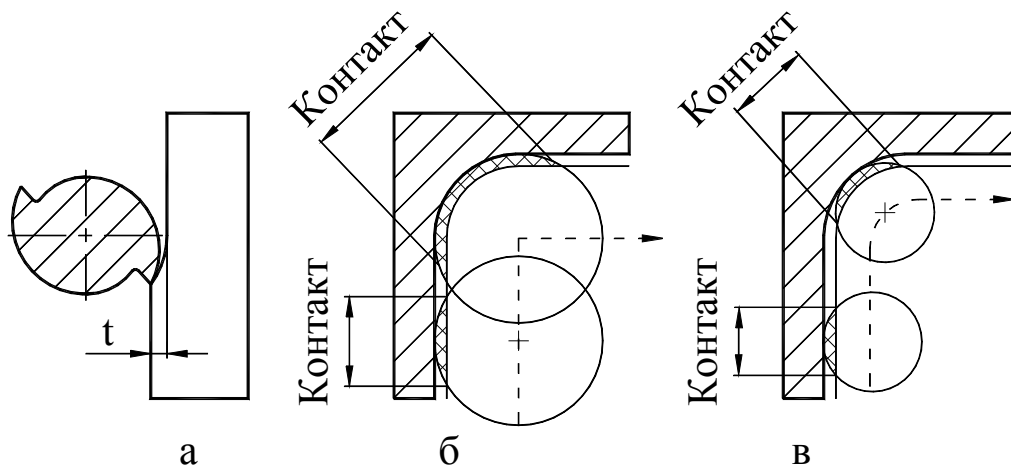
Особенности контакта инструмента с заготовкой при ВСО
